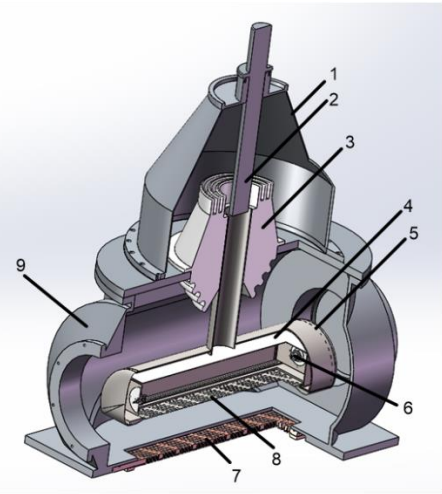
Ускоритель «ДУЭТ»: 1-колпак изолятора; 2-высоковольтный кабель; 3- изолятор; 4-полый анод; 5-корпус плазменного катода; 6-катодный узел; 7-выпускное фольговое окно; 8-маска; 9-вакуумная камера.
